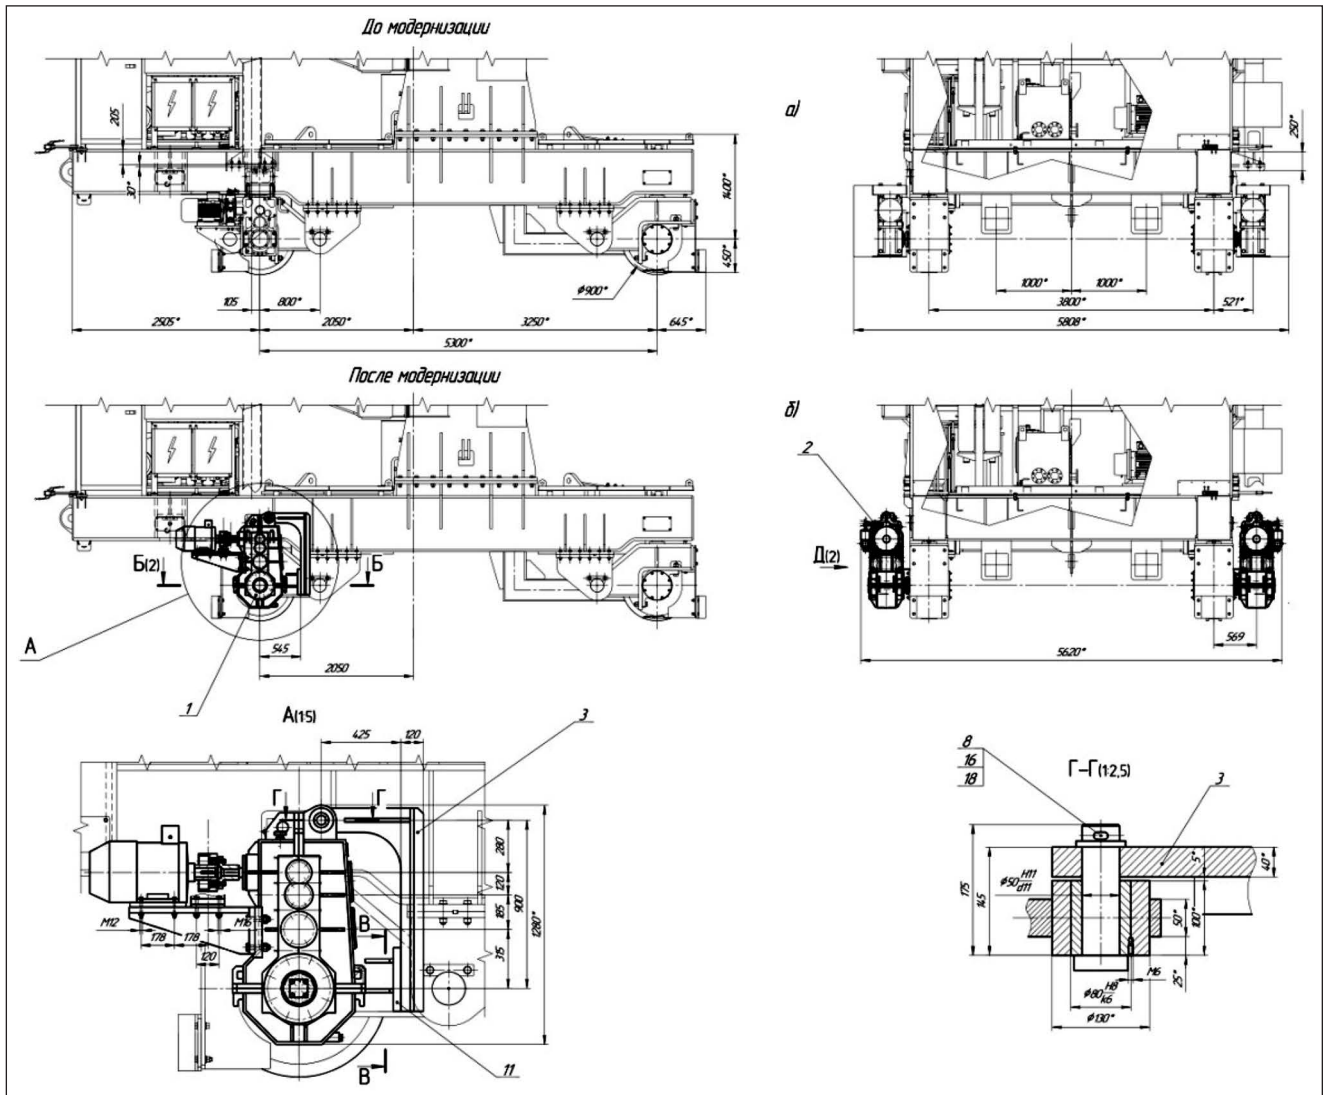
Привод механизма передвижения чугунозаливочной машины до (а) и после (б) модернизации: 1 — привод перемещения правый; 2 — привод перемещения левый; 3 — рычаг; 8 — палец; 11 — лист; 16 — шайба; 18 — шплинт
